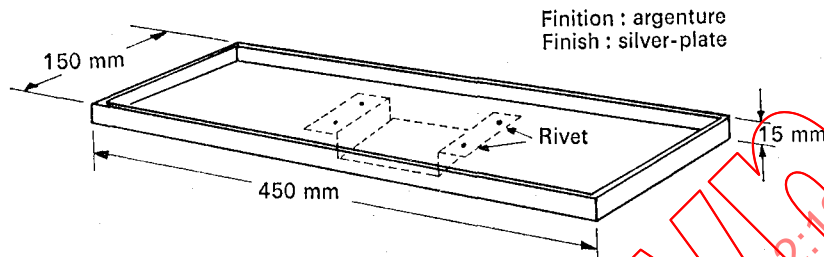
Disposition générale de la boîte d'essai (paragraphe 7.1).
